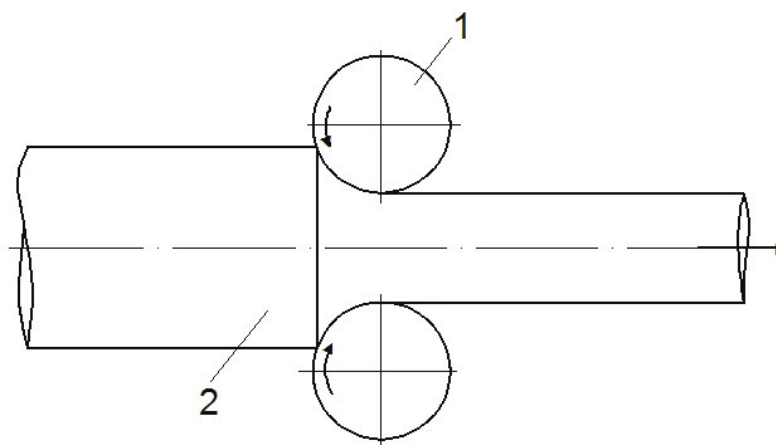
Схема продольной прокатки: 1 – валки, 2 – заготовка
